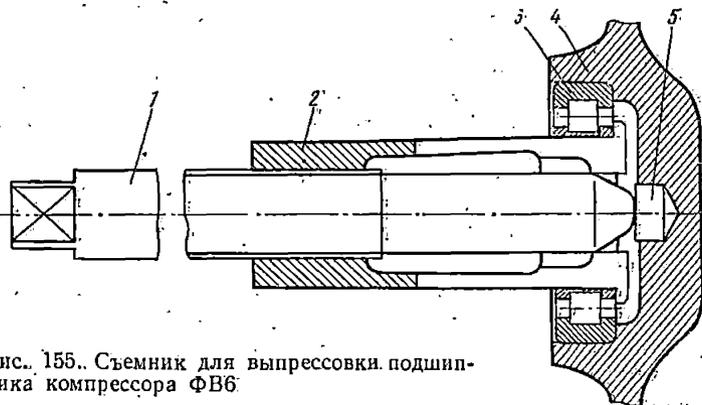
Съёмник для выпрессовки подшипника компрессора ФВ6
